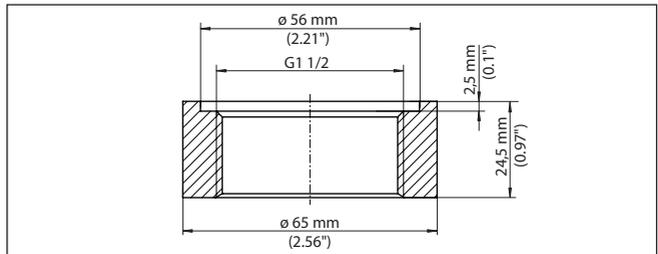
Dimensiones racor para soldar rosca G1½ (DIN 3852-X)
